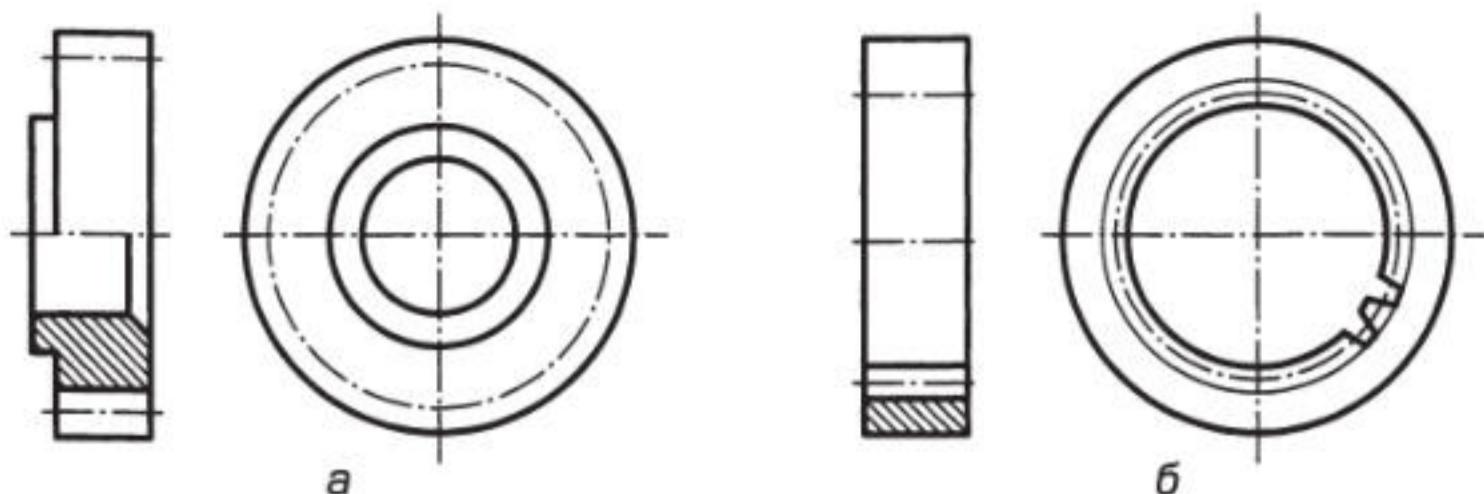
Условное изображение цилиндрических зубчатых колес с наружным (а) и внутренним (б) зубчатым венцом
